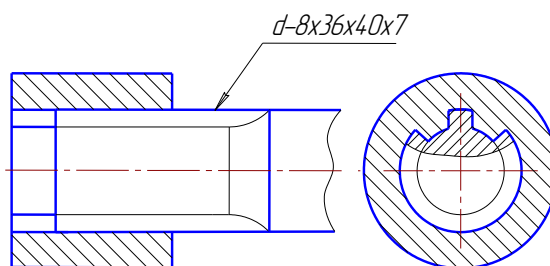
Изображение шлицевого соединения на сборочном чертеже
